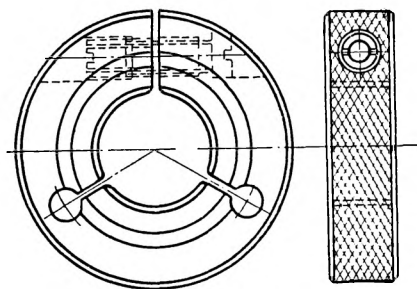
Регулируемый калибр для измерения наружной резьбы
